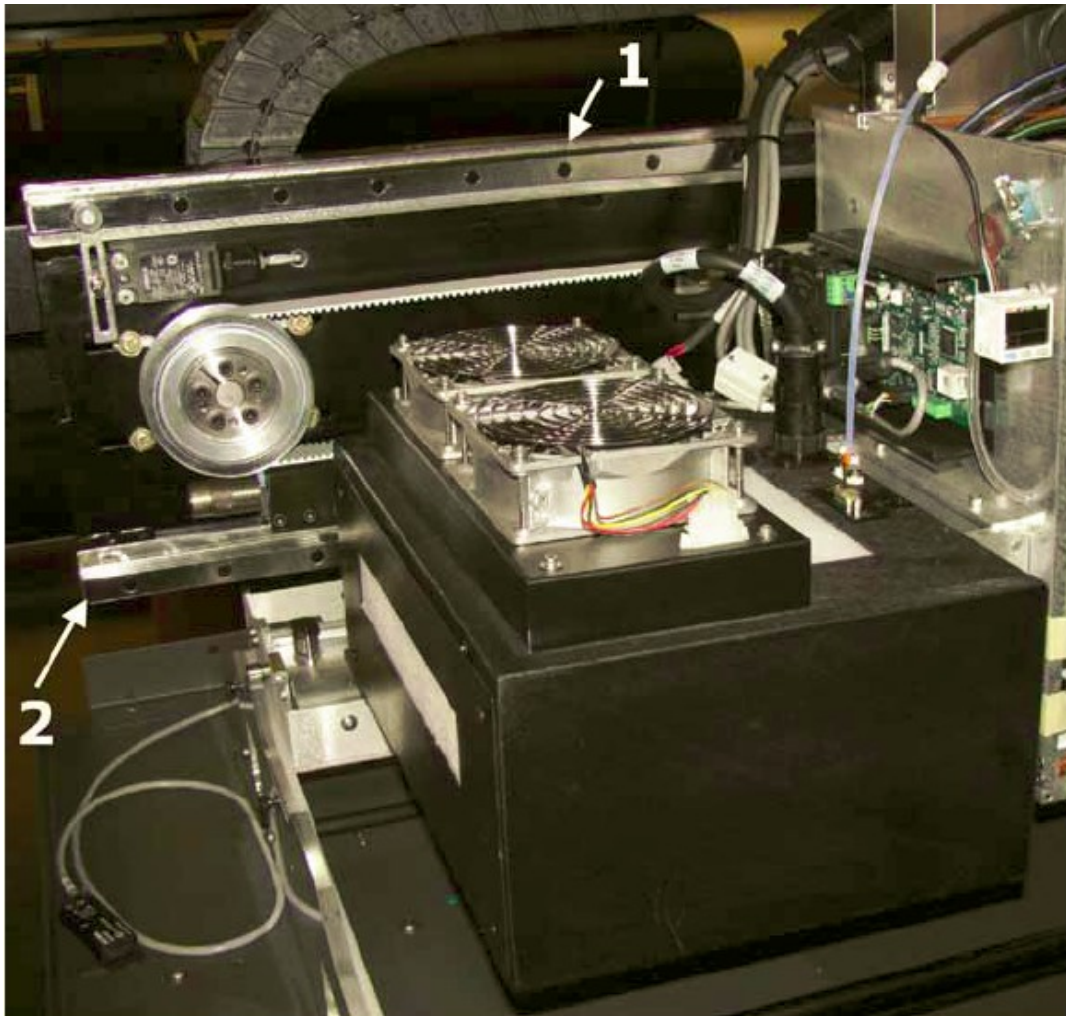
6: Рельсы, по которым перемещается печатная каретка
